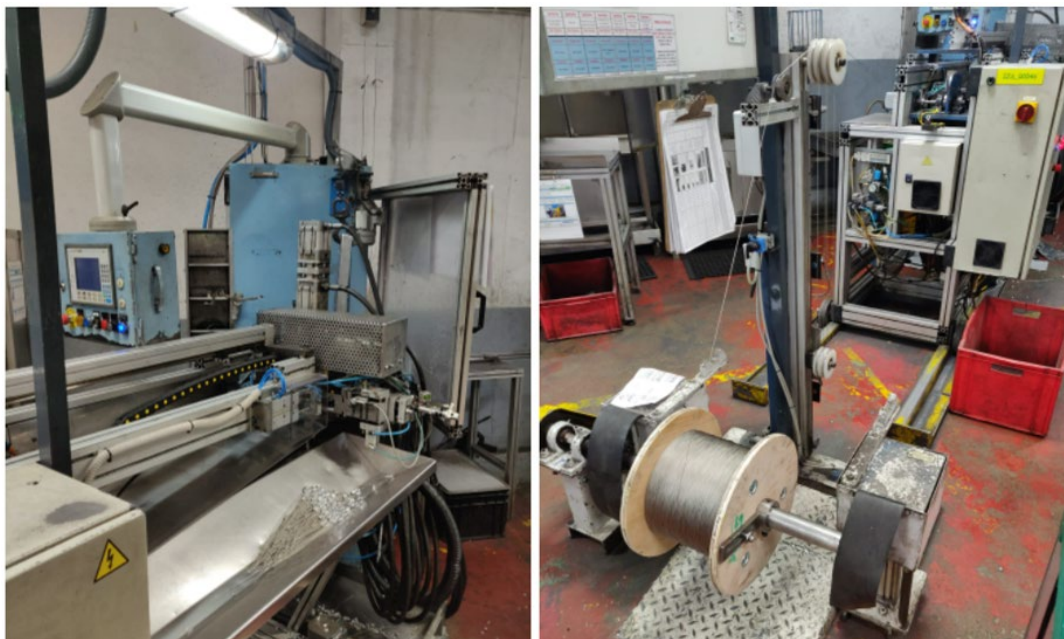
Máquina de injeção de zamak automática (*robocop*)
